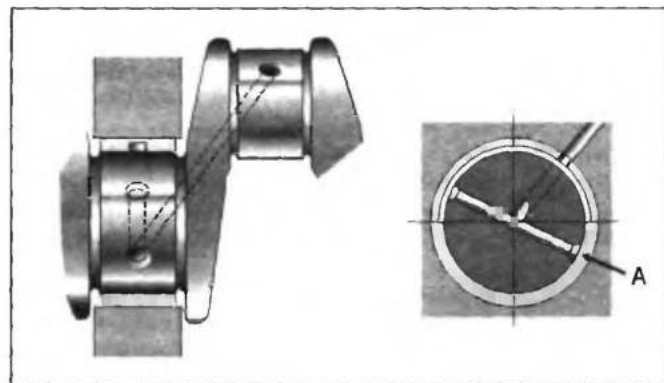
Наиболее распространенная схема смазки коренных подшипников коленчатого вала — верхний коренной вкладыш с канавкой, нижний — без канавки, А — сквозное отверстие в коренной шейке вала
